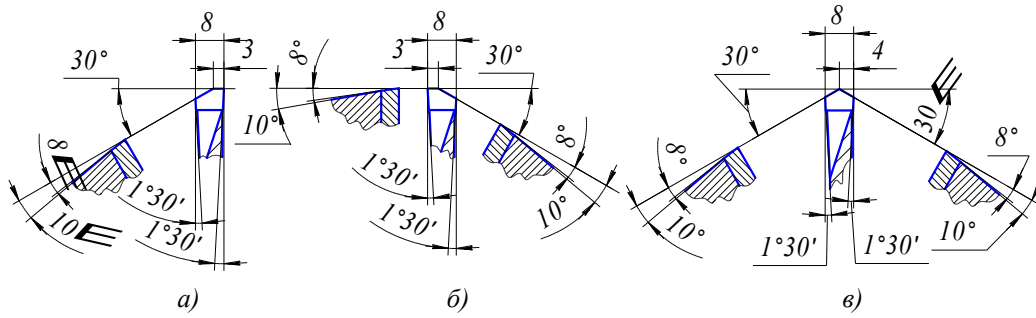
Заточування зубців кільцевого свердла з поділом стружки
